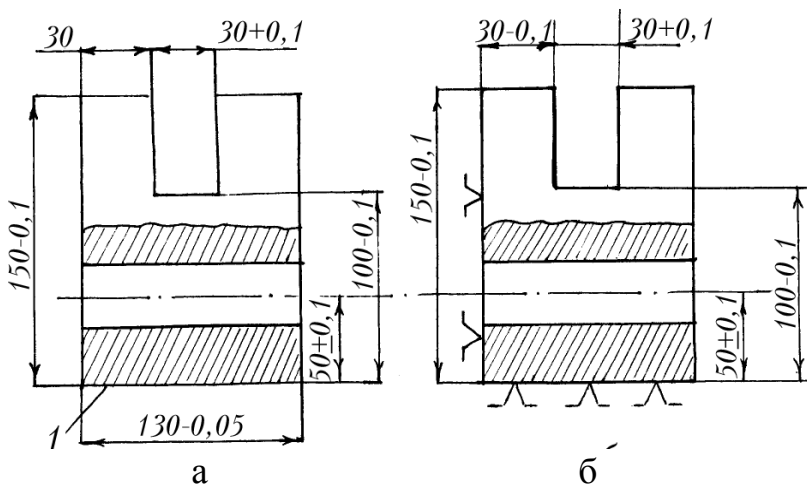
Креслення деталі (а) і операційний ескіз (б).
